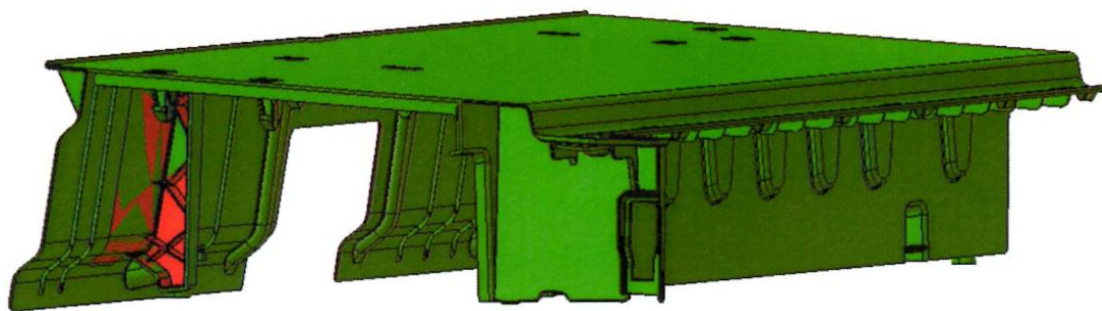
Superfícies da peça para o movimento à extração SI04.
